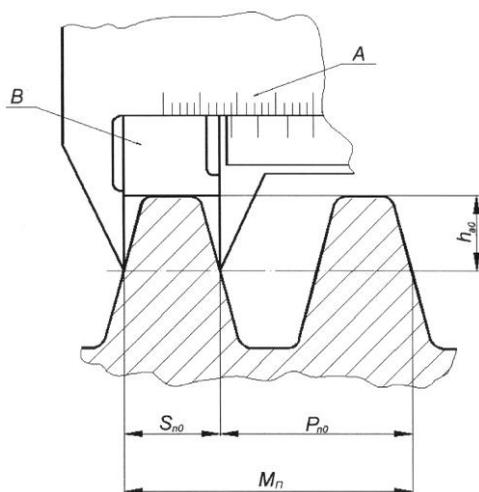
Схема измерения нормального шага винтовой спирали фрезы
